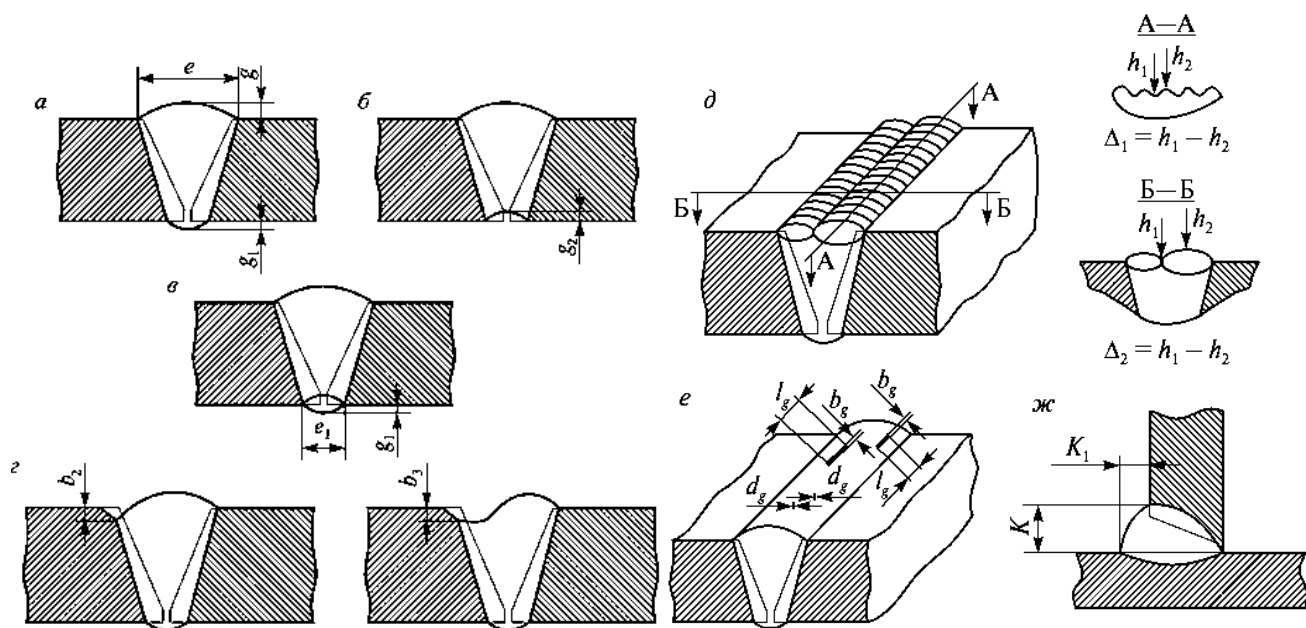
Конструктивные элементы и дефекты сварного шва, подлежащие измерительному контролю:
